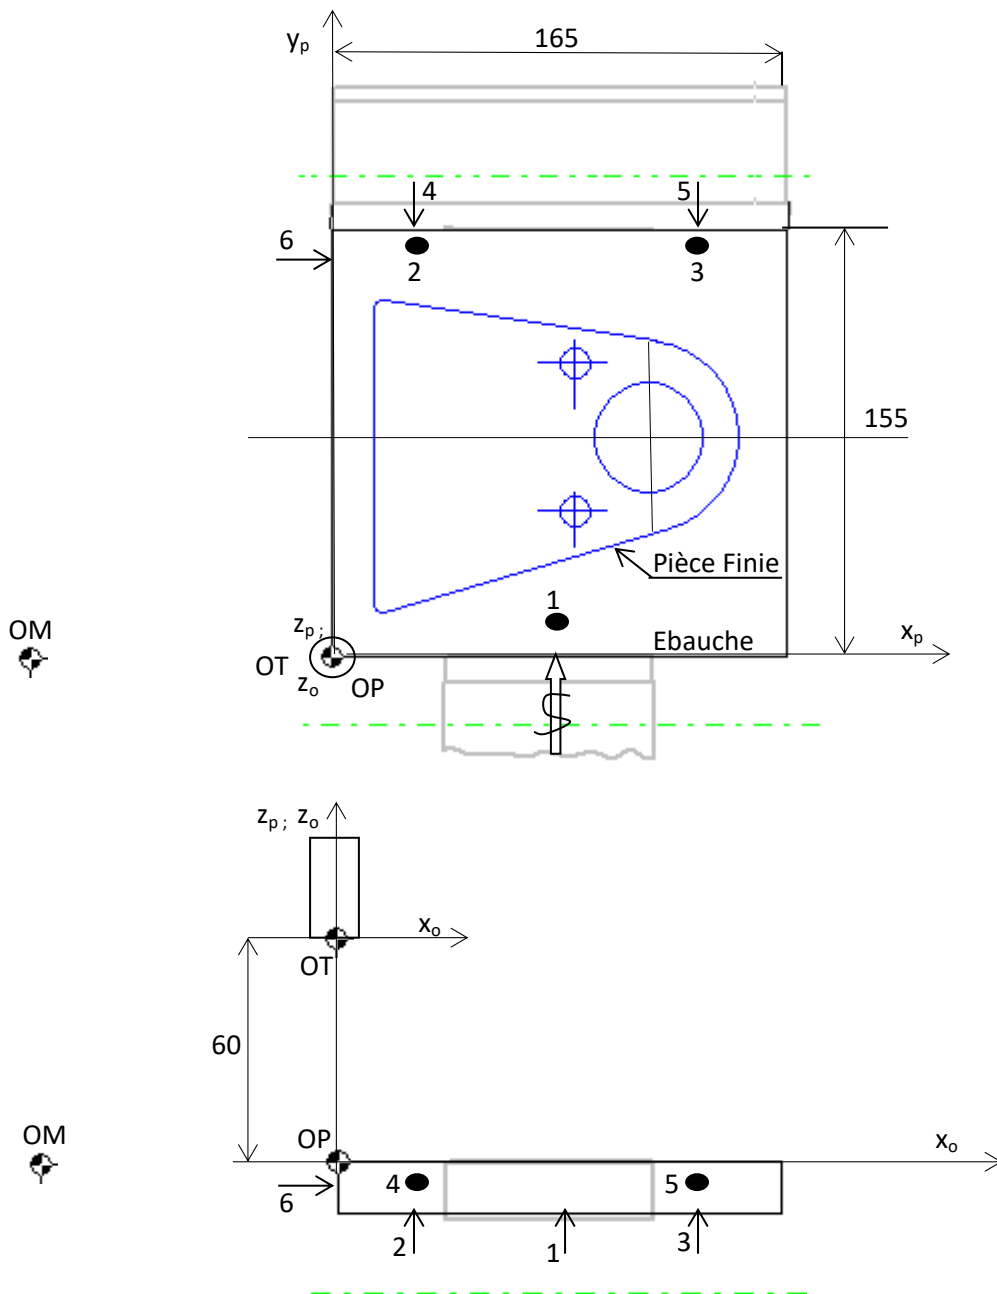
Schéma de réglage des cotes pour l'usinage de la chape
